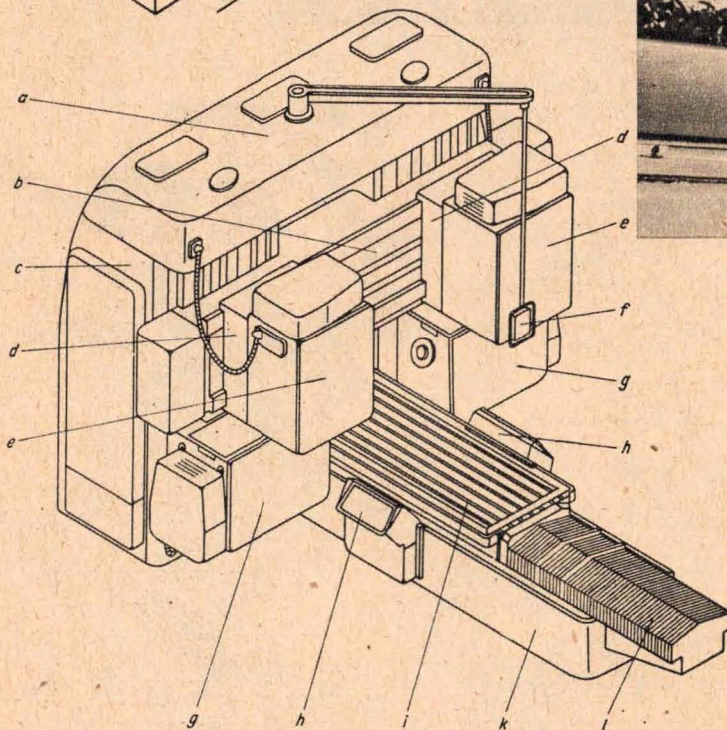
Prinzipieller Aufbau einer Bettfräsmaschine
